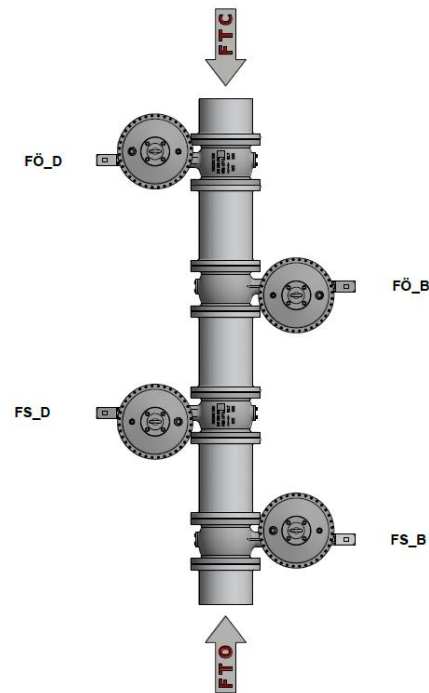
Alternative Einbaulagen: vertikale Rohrleitung (nach Rücksprache mit VETEC)
